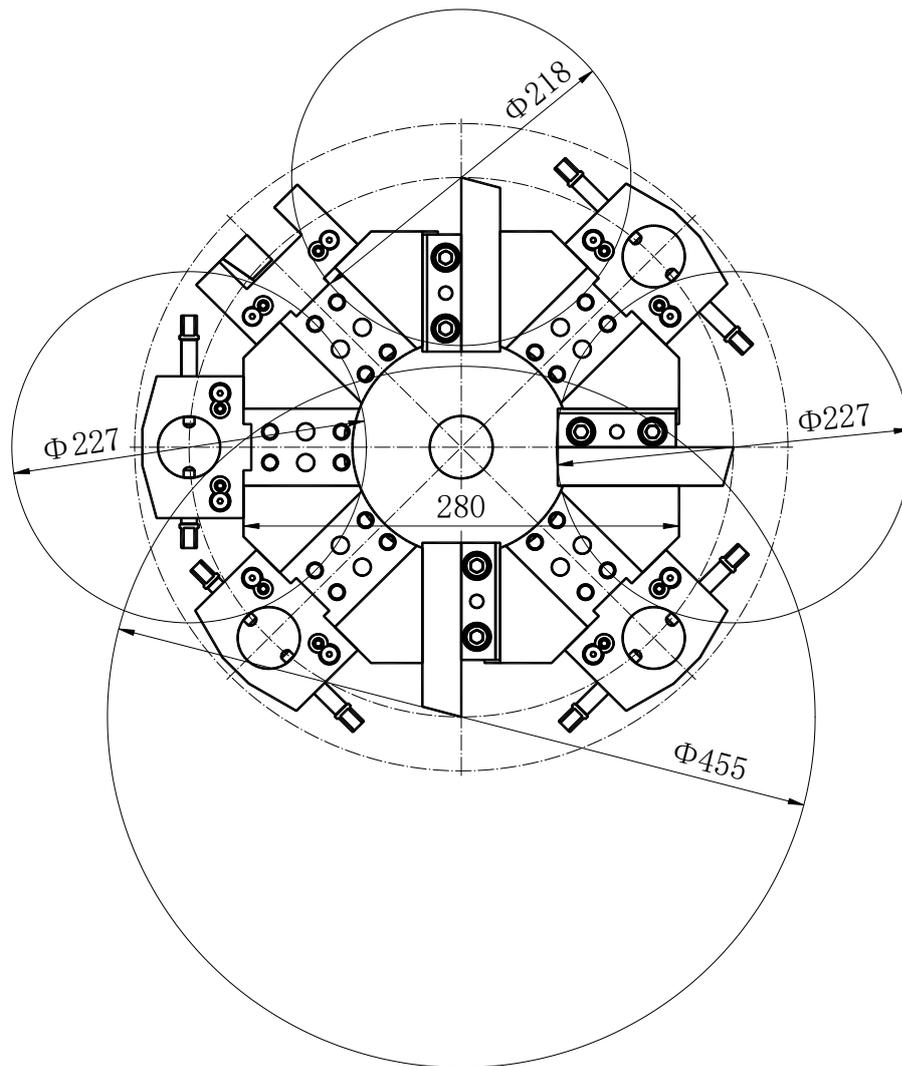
Структура диска инструмента и чертеж размера эталонной плоскости для монтажа инструмента
